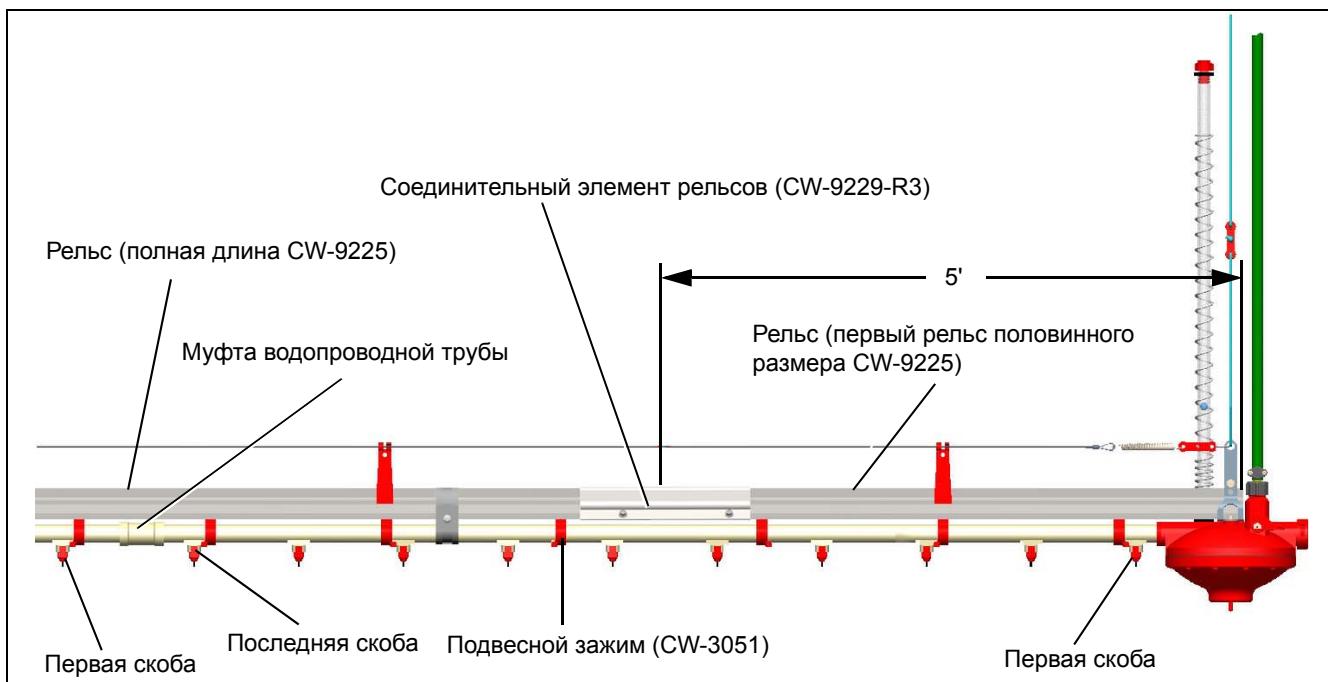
B Установка алюминиевого рельса, начиная с отрезка длиной 5'.
